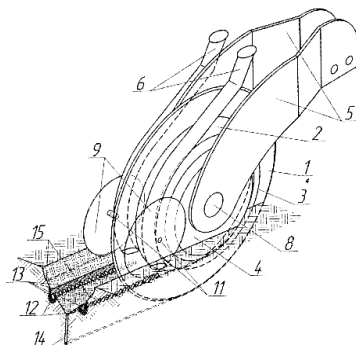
Технологическая схема работы комбинированного однодискового сошника с двусторонними ребордами и дисковыми загортачами для узкорядного посева: 1 – плоский диск; 2 – внутренняя реборда; 3 – бороздкообразователь; 4 – наружная реборда; 5 – корпус; 6 – семянаправители; 8 – ось; 9 – сферические диски; 11 – ось; 12 – ложе; 13 – семена; 14 – щель; 15 – бороздки
